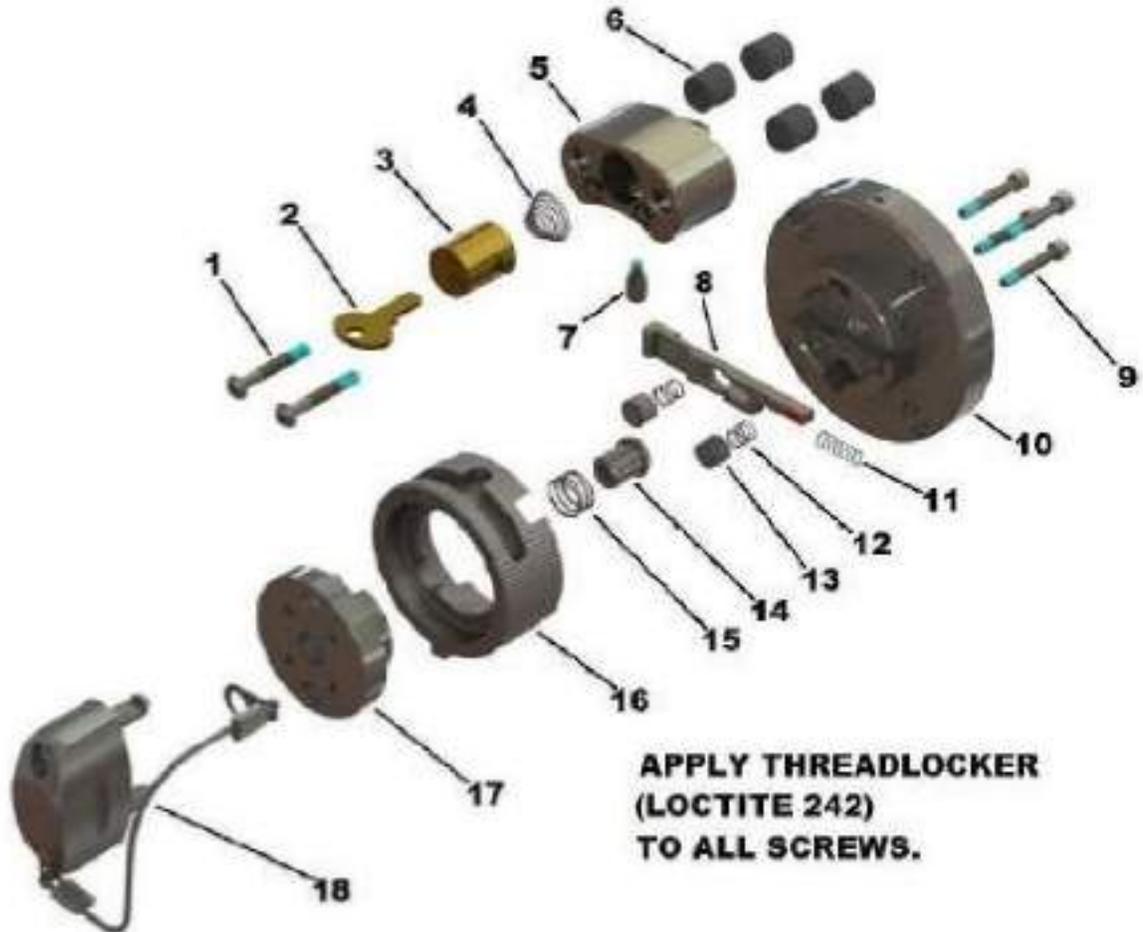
Vue éclatée des composants de l'assemblage du collimateur
